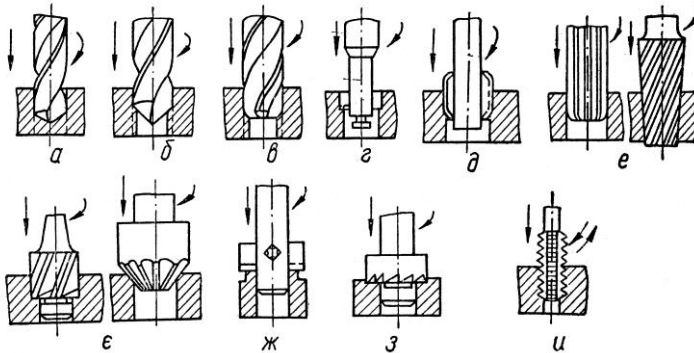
Основні види свердильних робіт: а – свердління; б – розсвердлювання; в – зенкерування; г,д – розточування отворів; е – розвертання; є – зенкування; ж,з – цекування; и – нарізання різьби
